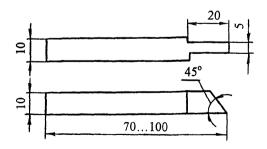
Боек для изготовления искусственных дефектов типа зарубок
